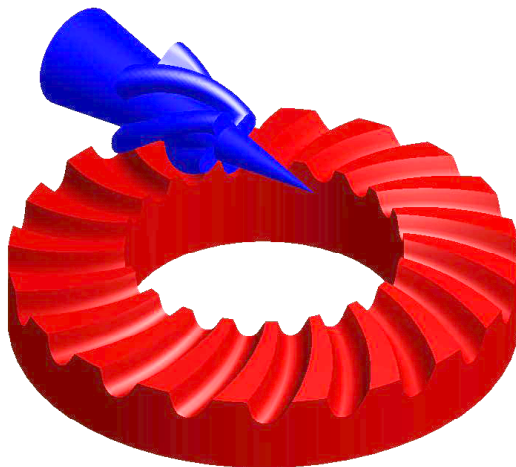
Детали конической гипоидной передачи: шестерня (4 зуба) и колесо (20 зубьев)
